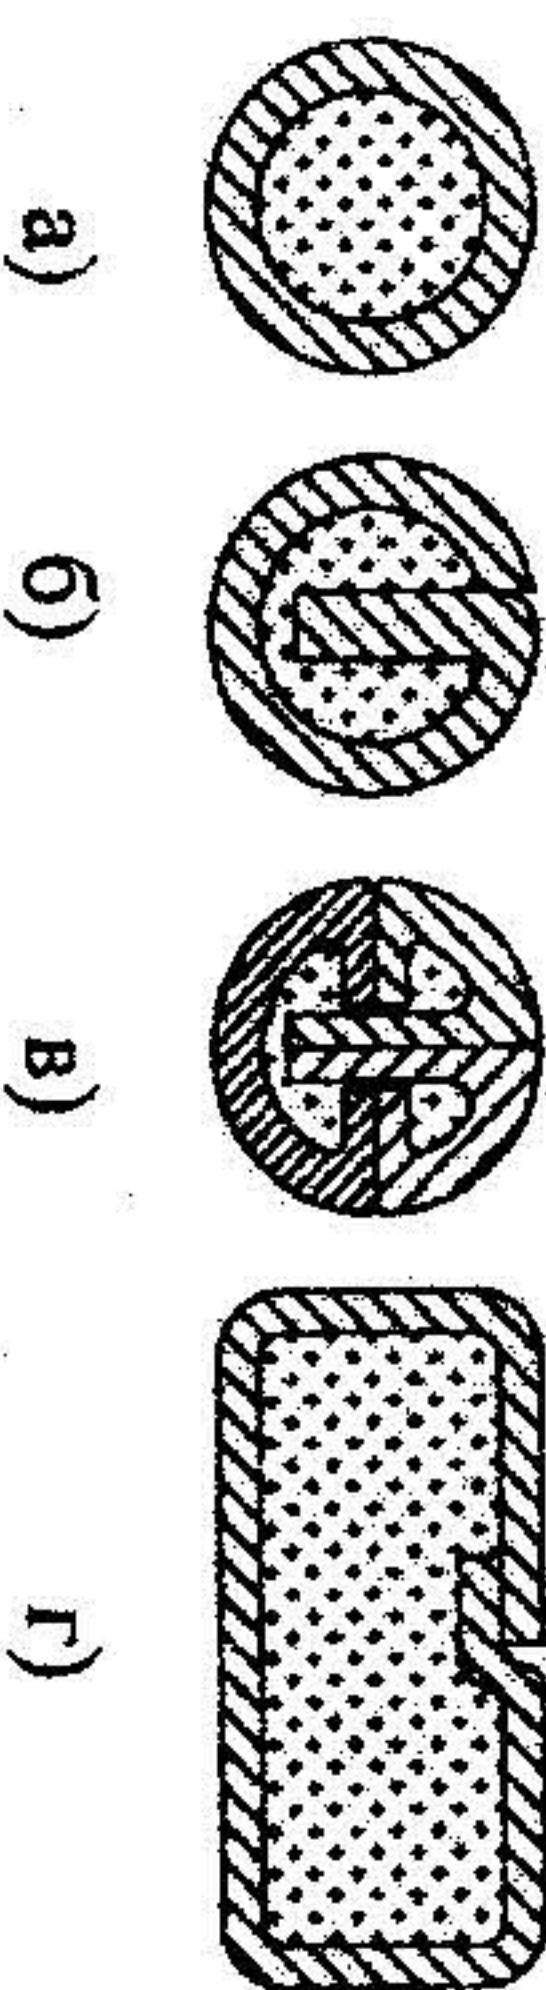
Основные конструкции порошковых проволок для наплавки:
